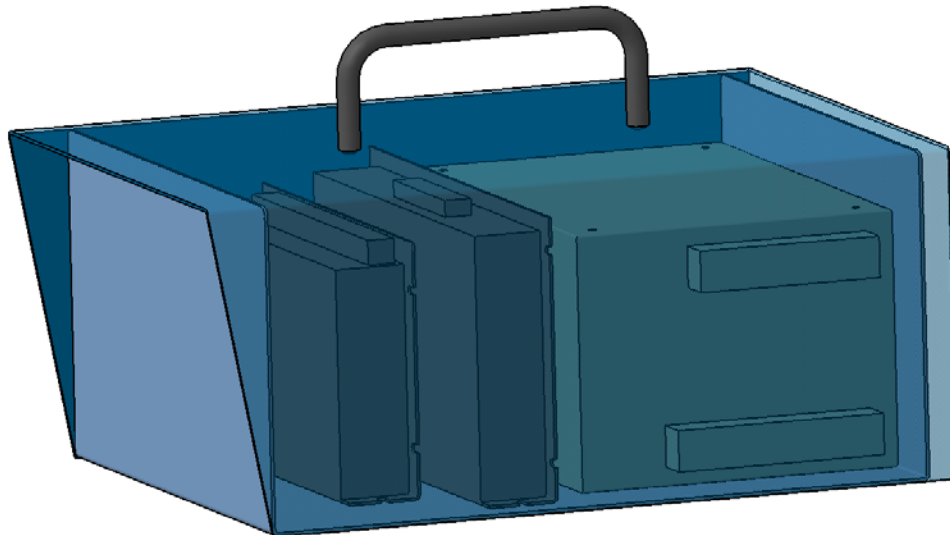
Zeichnung der Steuerbox mit halblattem Deckel. Hinten, quaderförmig: Netzteil, davor, flach: Brems-Chopper und Motorsteuerung.
